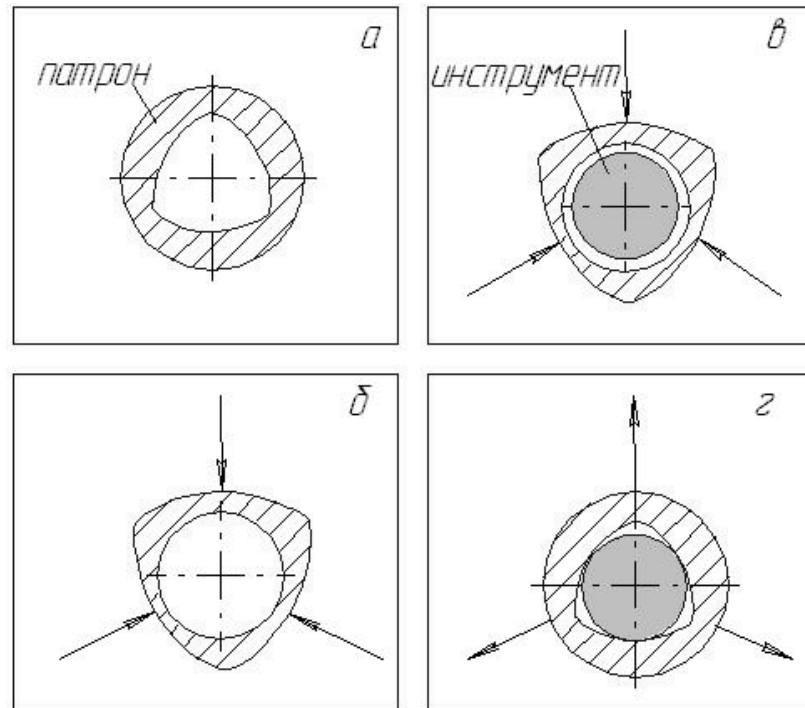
Принцип закріплення інструменту у патроні Tribos [9]
